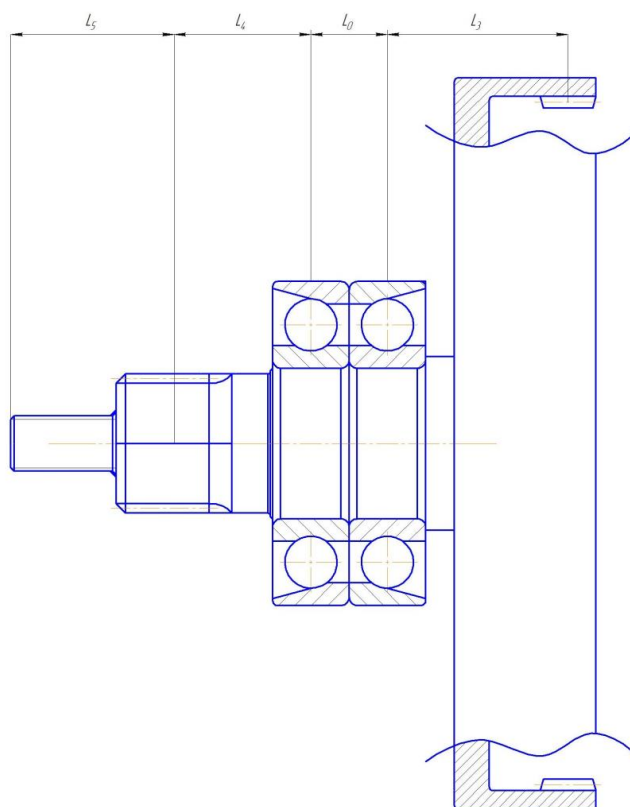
Компоновка ведомого вала заднего колесного редуктора
